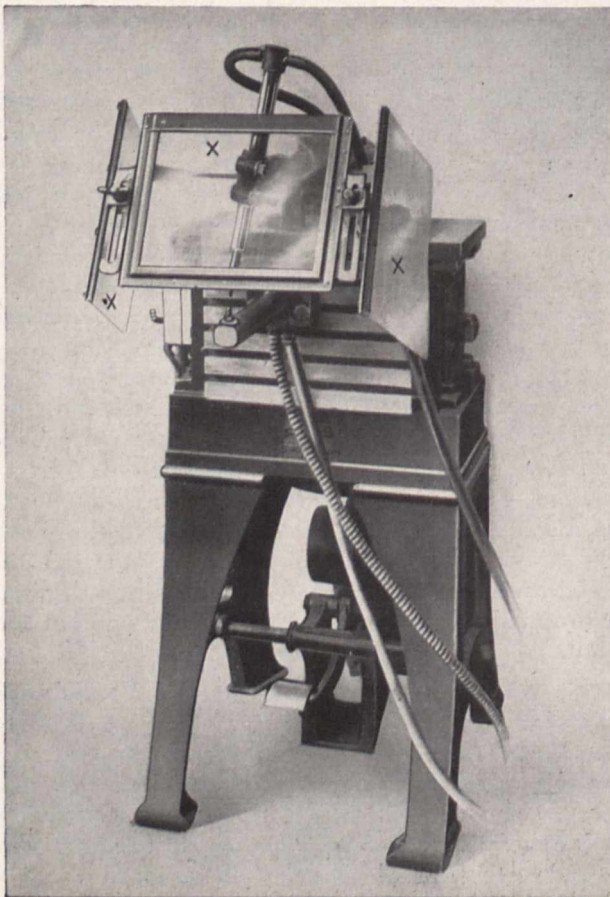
, Schutzvorrichtung an elektrischen Schweißmaschinen
